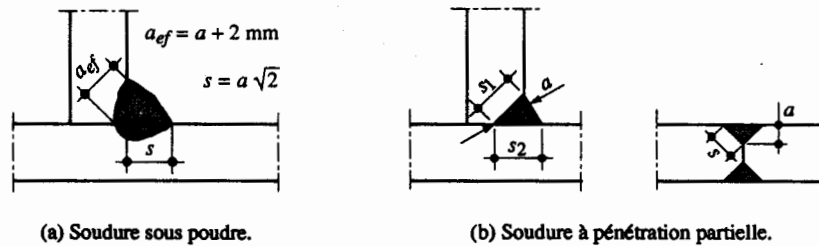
Définition des sections de calcul des soudures sous poudre et à pénétration partielle.
